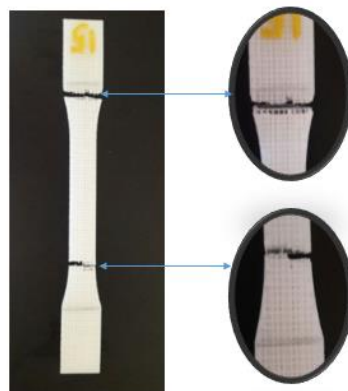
Fractura de probetas a) Probeta 17 Ciclo de Exposición A. b) Probeta 26 Ciclo de Exposición B.
